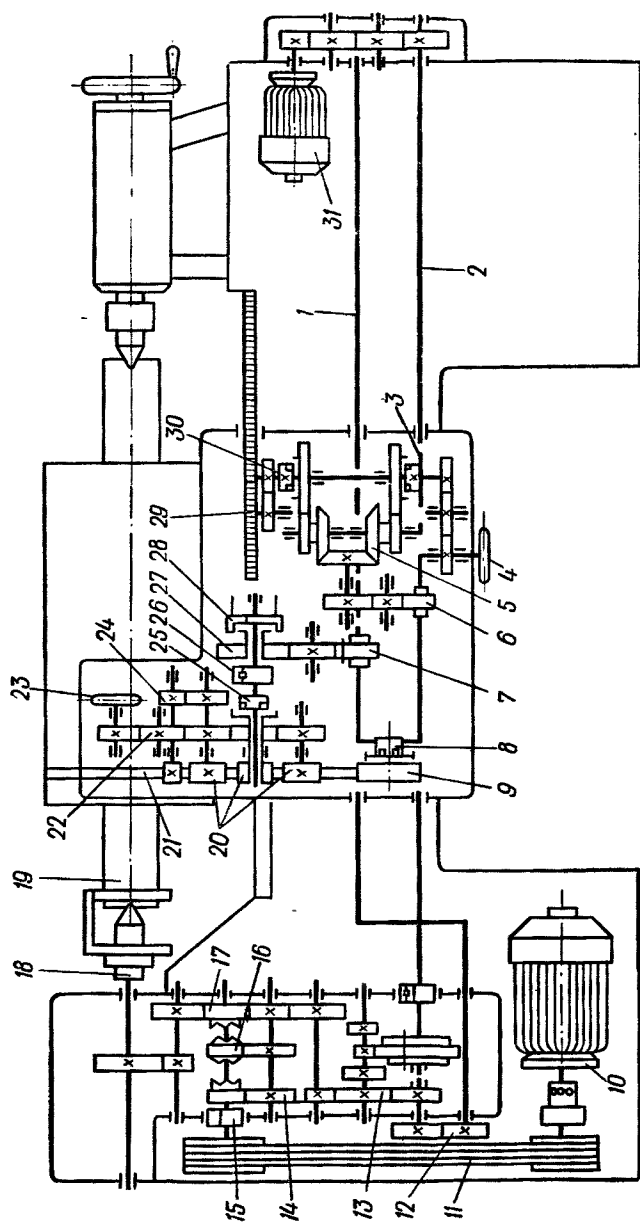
Кинематическая схема полуавтоматического станка для намотки бандажей из стеклолоты
